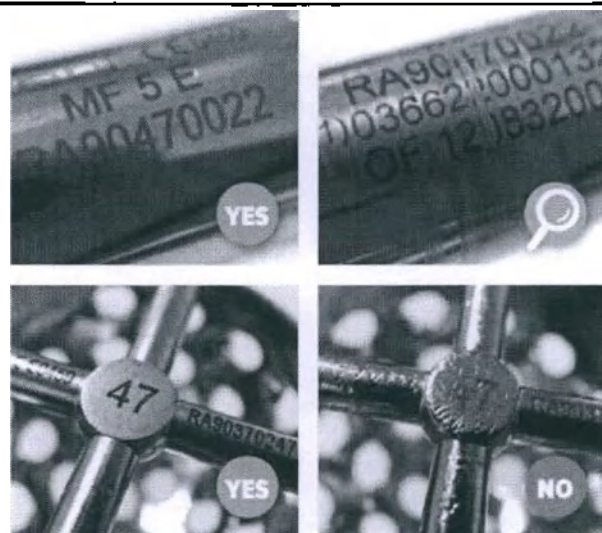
Точность лазерной маркировки / Figure 70. Wearing of laser marking,
